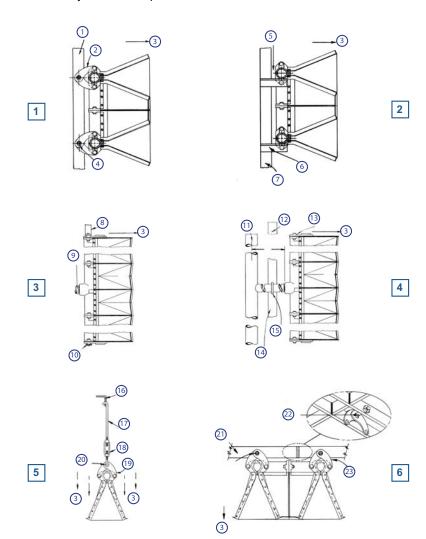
горелка, подвешанная на раме из полосовой стали с помощью крепежных скоб Maxon USB. Обратите внимание, что отверстие скобы не плотно обхватывает болт металлический стержень, за счет чего удается избежать жесткой стыковки деталей. Линия газового трубопровода требует отдельного крепления.
